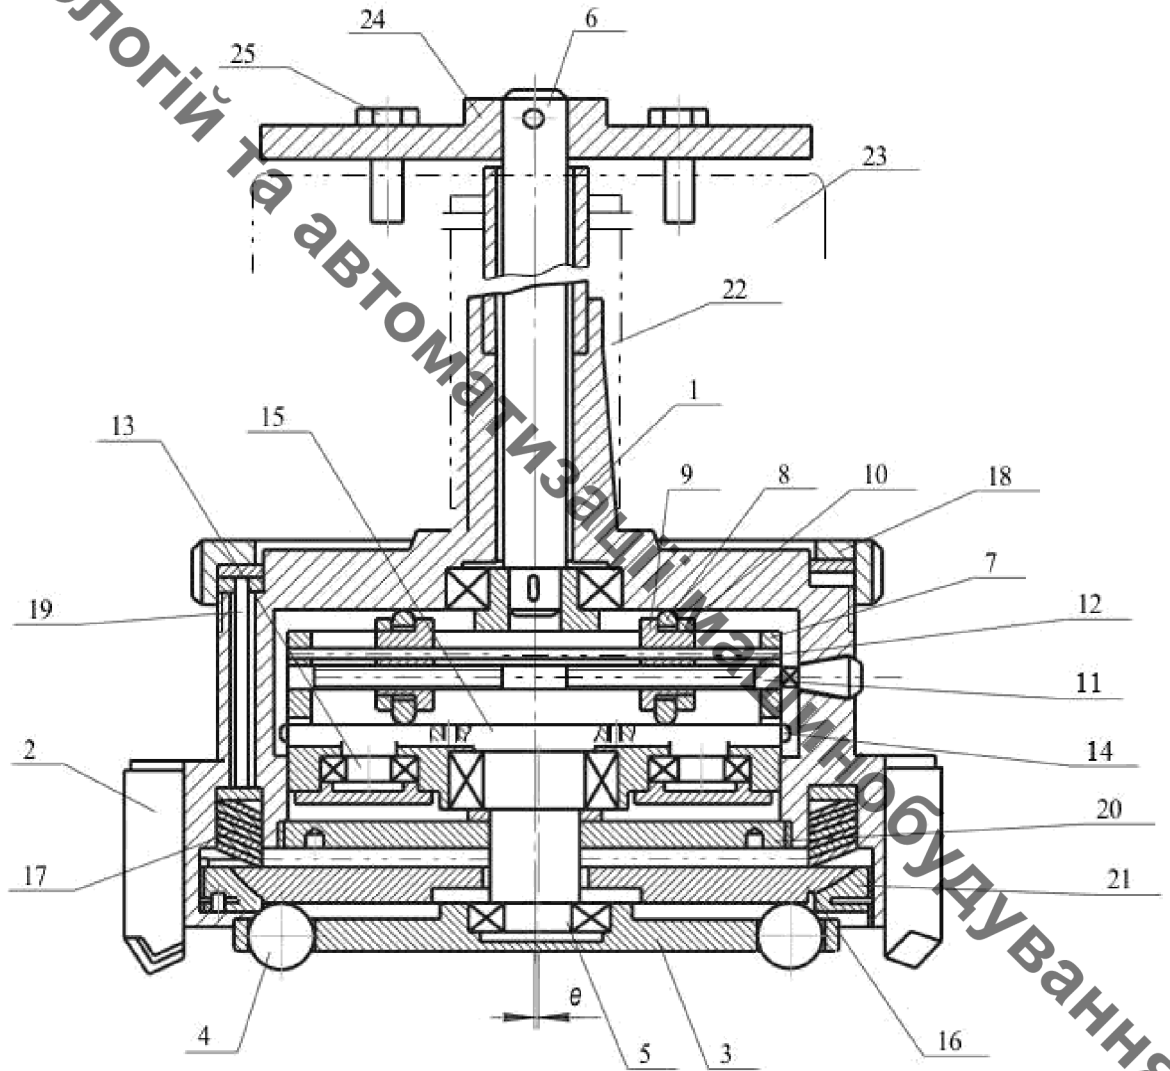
Пристрій для комбінованої обробки плоских поверхонь
